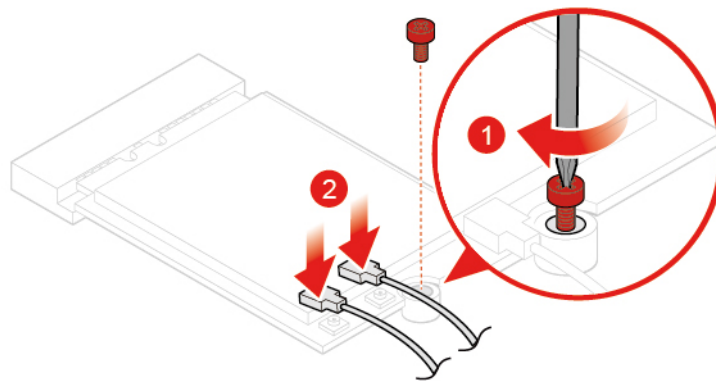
Collegamento dei cavi dell'antenna Wi-Fi
